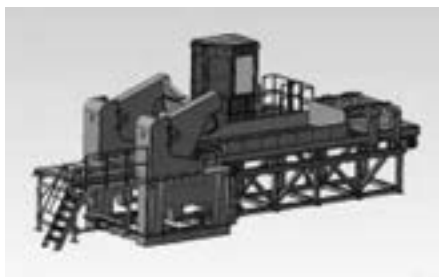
Мобильные установки по переработке железобетонных конструкций.
